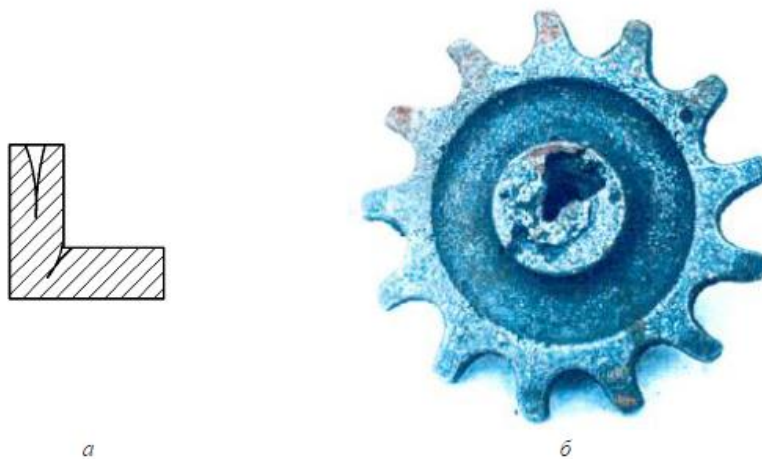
Дефект – усадочная раковина: а – схема; б – дефектная отливка
